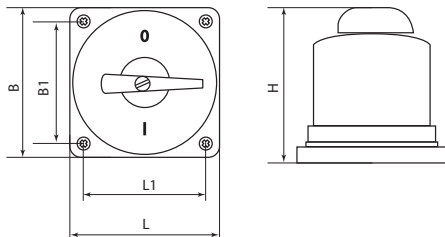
Схемы габаритных размеров пакетных выключателей в корпусе из карболита IP30
